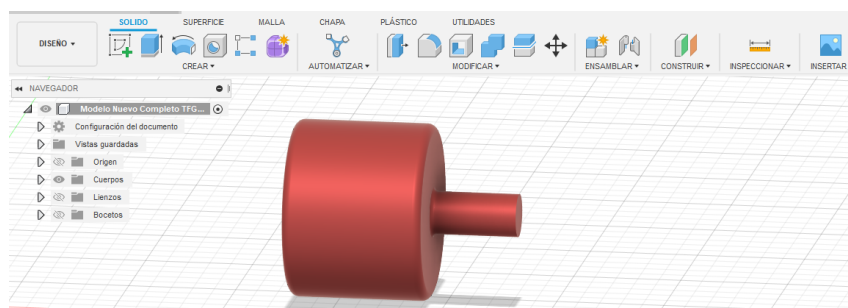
Diseño de motor en Fusion 360. (fuente propia)
